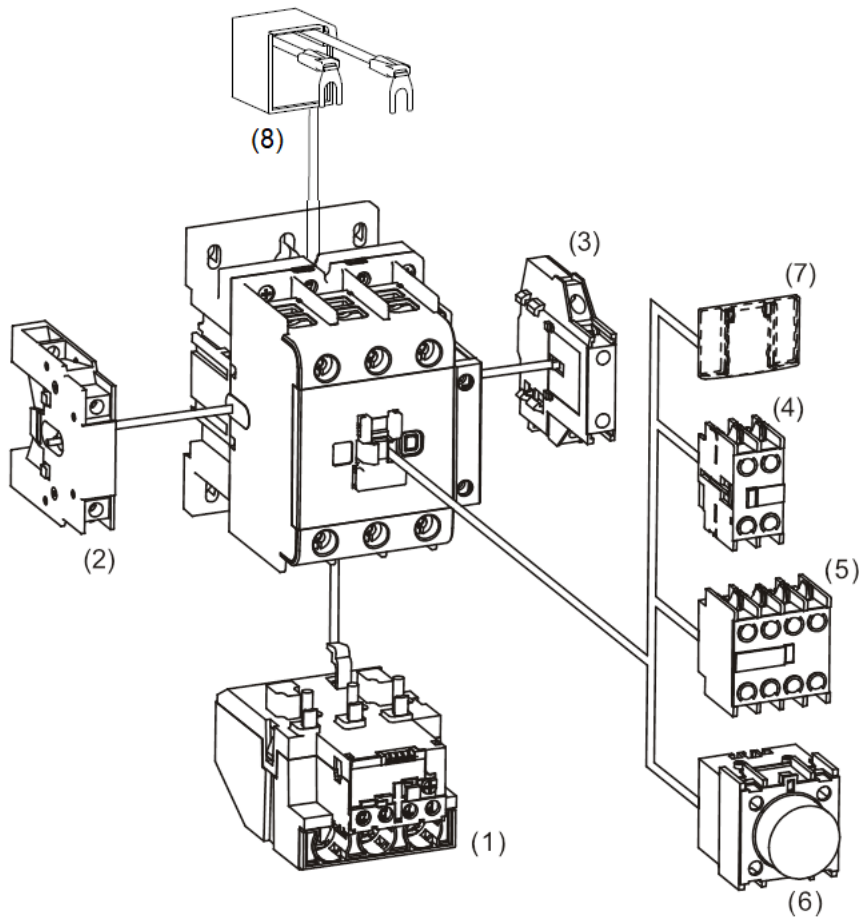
Контактор КМ-102 и схематичная установка аксессуаров
